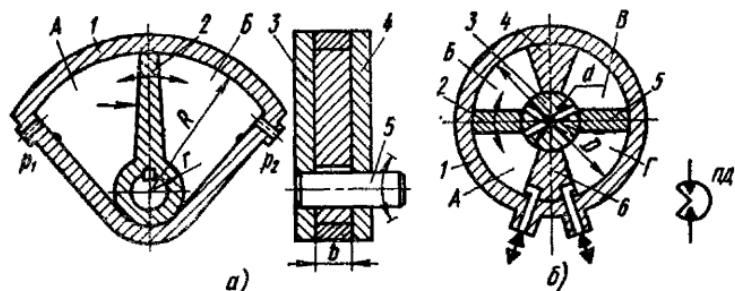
Однопластинчатый (а) и двухпластинчатый (б) поворотные гидродвигатели
